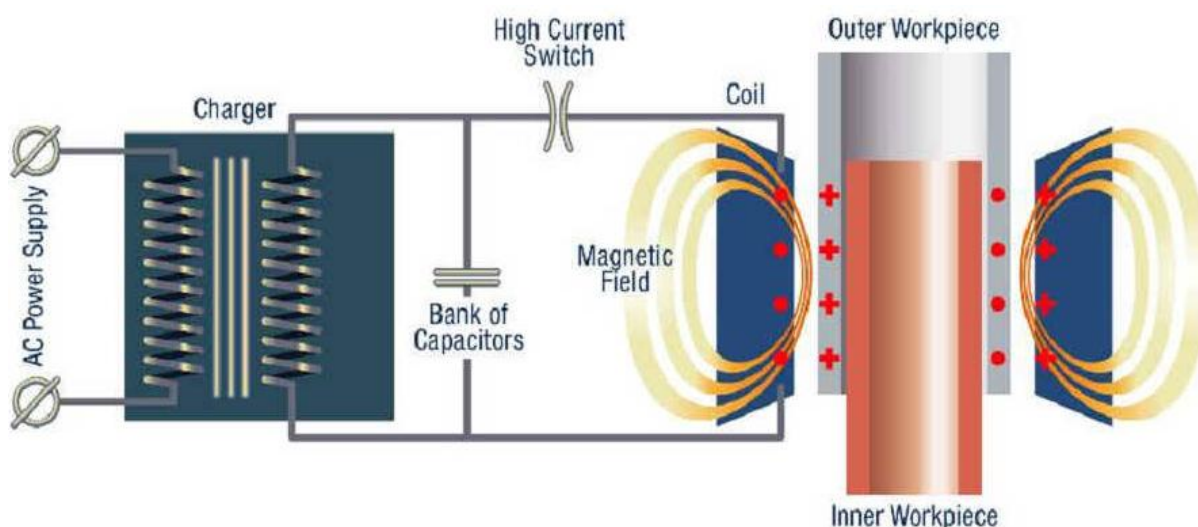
Schéma de principe du soudage par impulsion magnétique [54].
